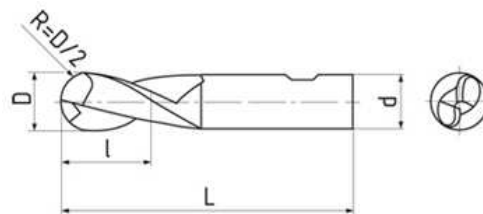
Fréza pro drážky per krátká (interní zdroje)
